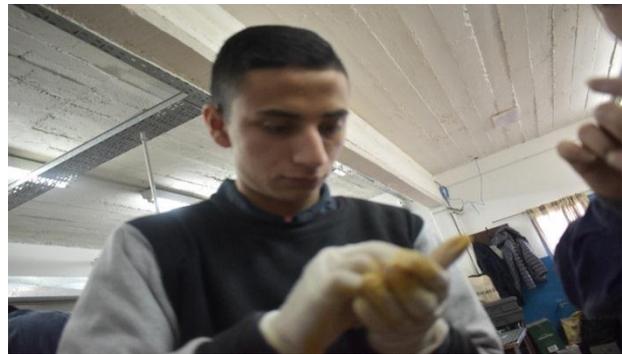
Seccionado de la placa de cobre para fabricar la placa y posterior al paso por acido cloruro férrico.
